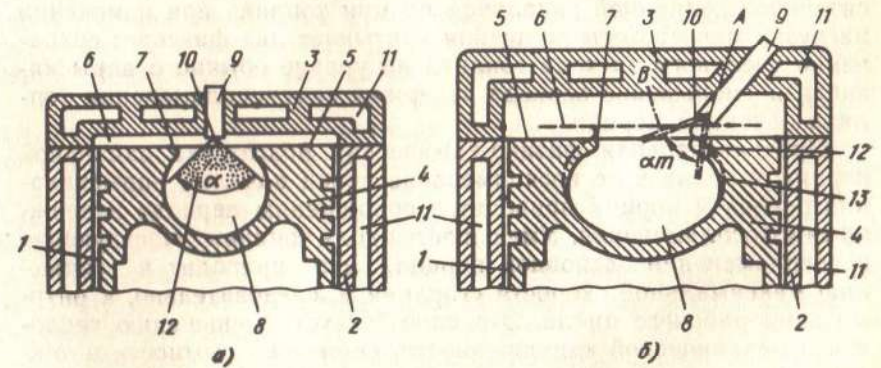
Камера сгорания, реализующая объемный процесс смесеобразования с вертикальным (а) и наклонным (б) расположением форсунки: 1 — боковая поверхность поршня; 2 — цилиндр; 3 — головка цилиндра; 4 — поршень; 5 — днище поршня; 6 — надпоршневой зазор; 7 — горловина поршня; 8 — камера в поршне; 9 — форсунка; 10 — основание струи; 11 — рубашка охлаждения; 12 — факел топлива; 13 — проточка в горловине
